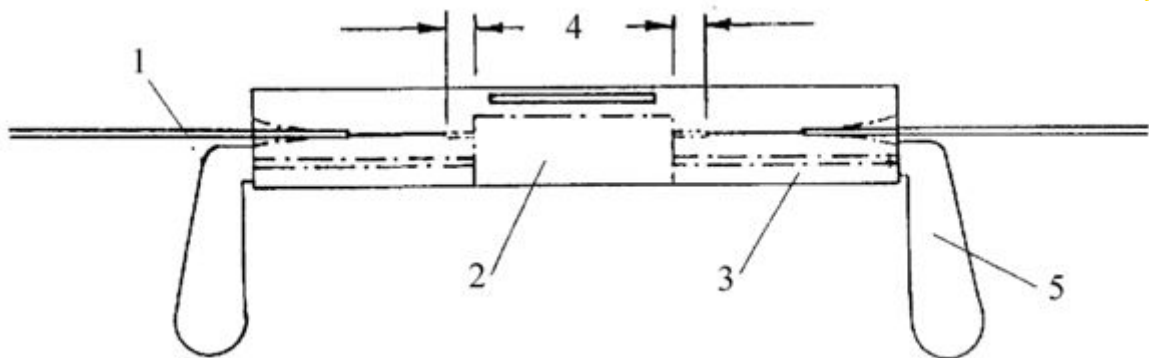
Механічний з'єднувач CORELINK: 1 – ОВ, 2 – алюмінієвий елемент для юстирування, 3 – прозорий корпус, 4 – зазор для запобігання пошкодженню торців ОВ, 5 – спеціальний ключ для розсування стінок корпуса на кут 90°
